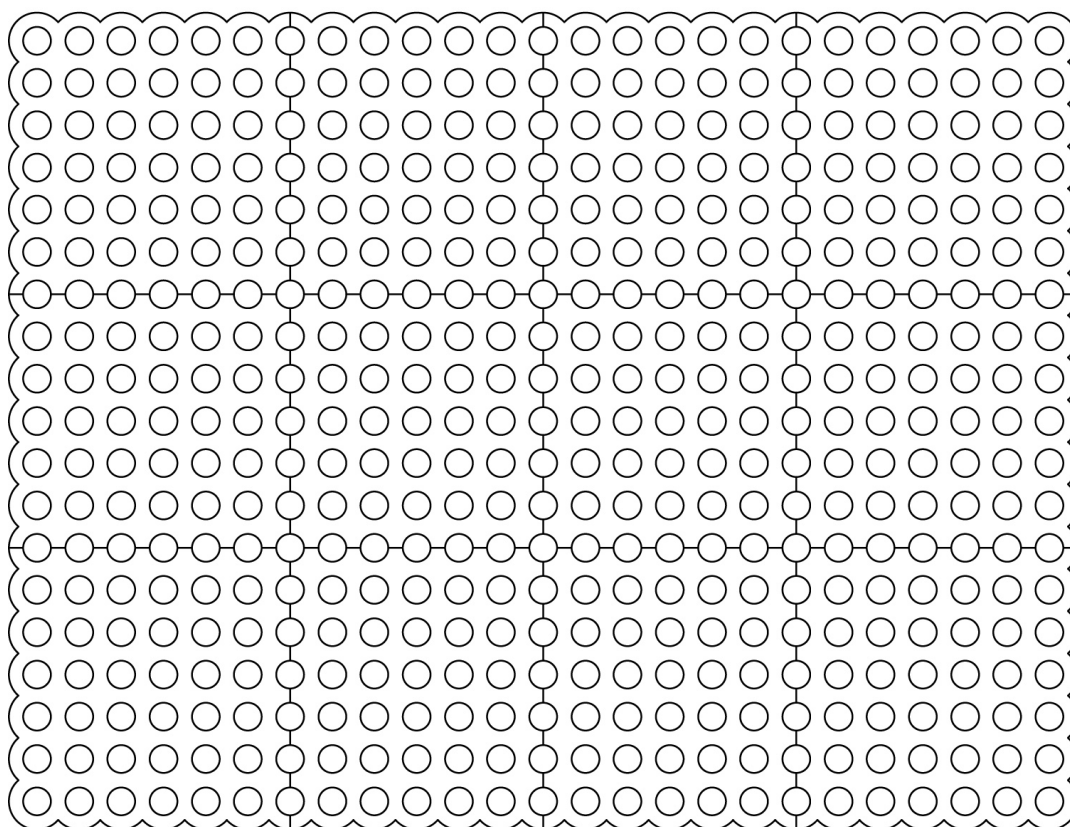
Vista Frontal de conjunto das peças da 2ª camada.
